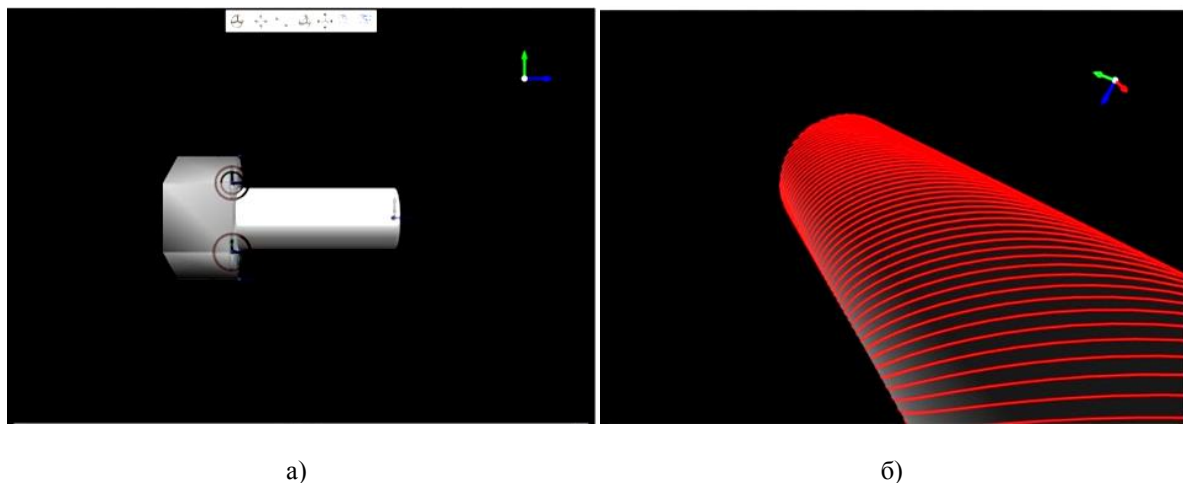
Модель болта, різьбова частина: а) модель болта, вид збоку, б) модель різьбової частини болта
